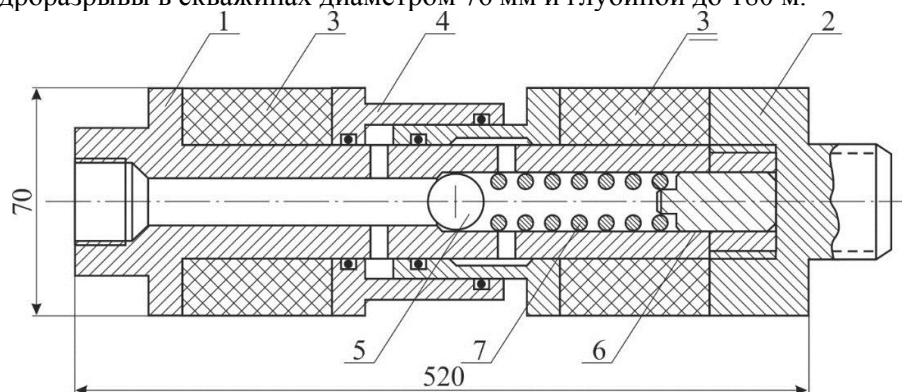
Схема полиуретанового уравновешенного герметизирующего устройства состоит: 1 – корпус; 2 – забурник; 3 – втулка полиуретановая; 4 – гидроцилиндр; 5 – клапанный блок; 6 – регулировочный винт; 7 – пружина
